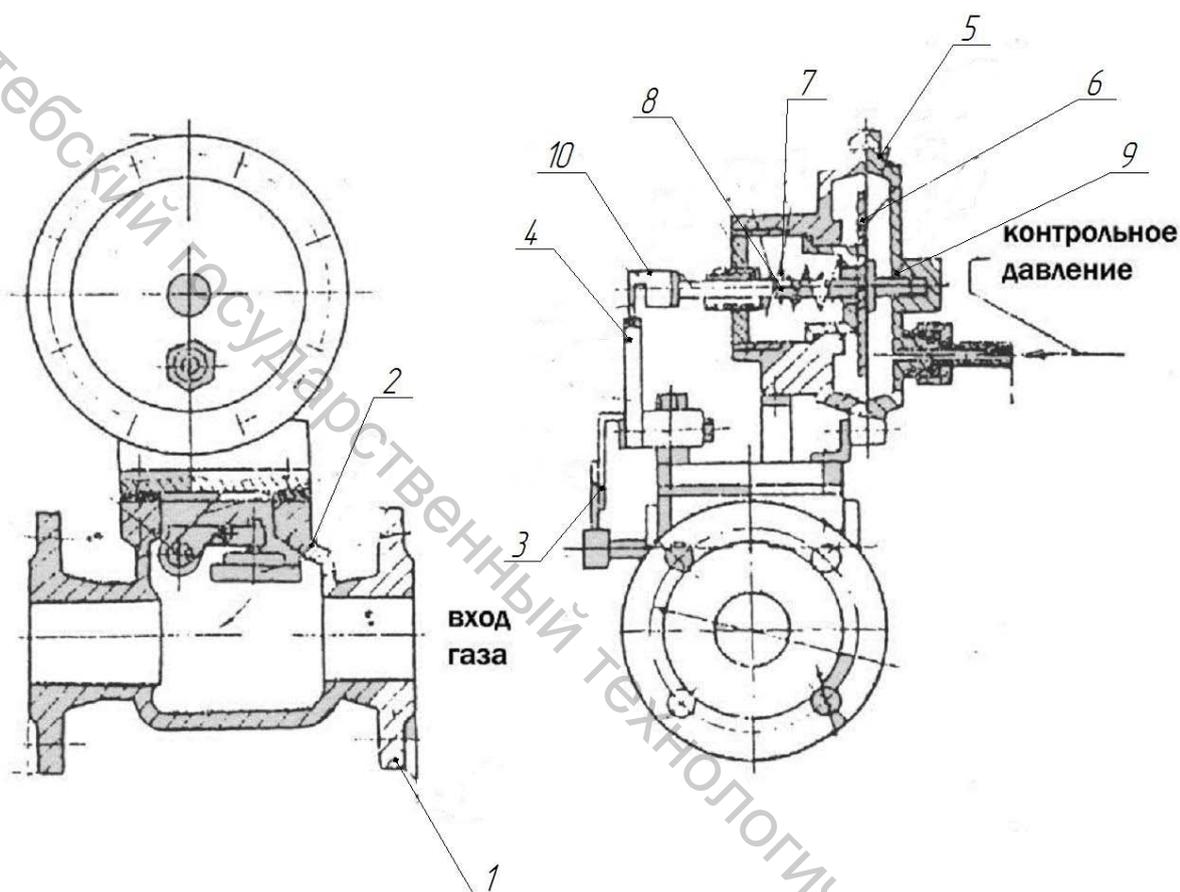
Предохранительно-запорный клапан КПЗ
